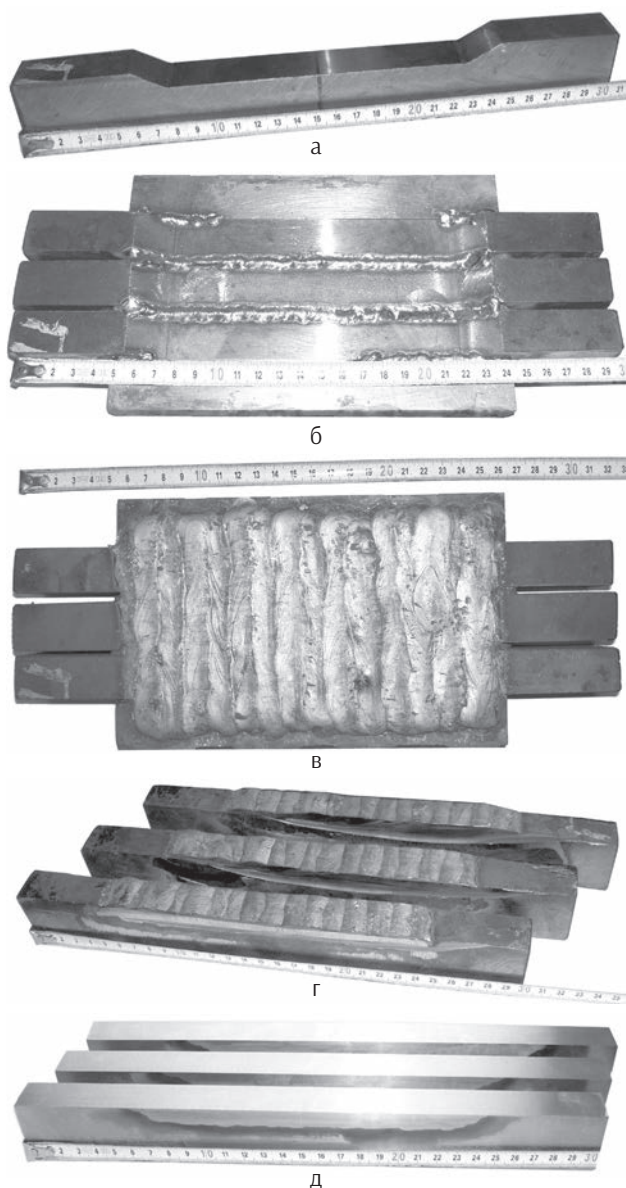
Этапы изготовления наплавленных образцов: заготовка с разделкой под наплавку (а); заготовки, собранные в пакет (б), после наплавки (в), порезки (г) и финишного шлифования (д)
